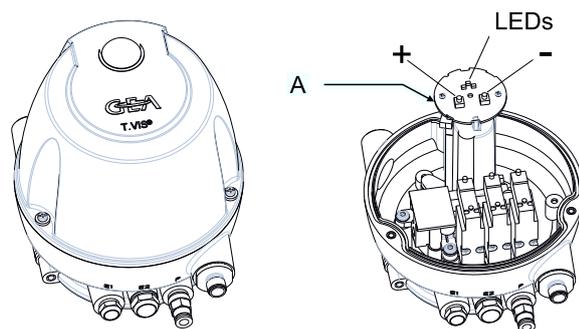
Steuerkopf mit Haube inklusive Taster (Standard-Variante in IP66)
